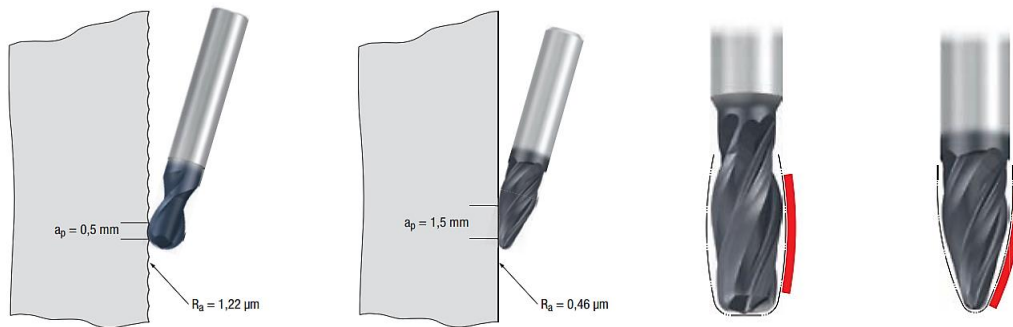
25 Pasada con fresa esférica y de barril. Diseños de fresa de barril de Emuge-Franken
